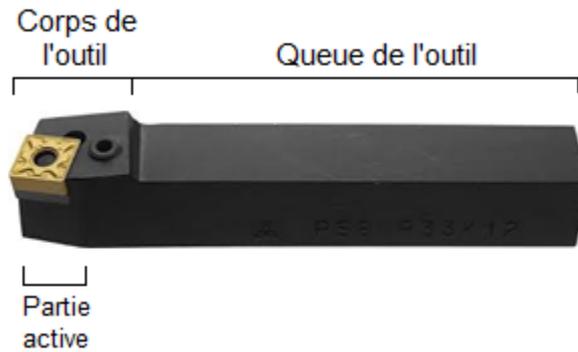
principales surfaces d'un outil de coupe [16]
